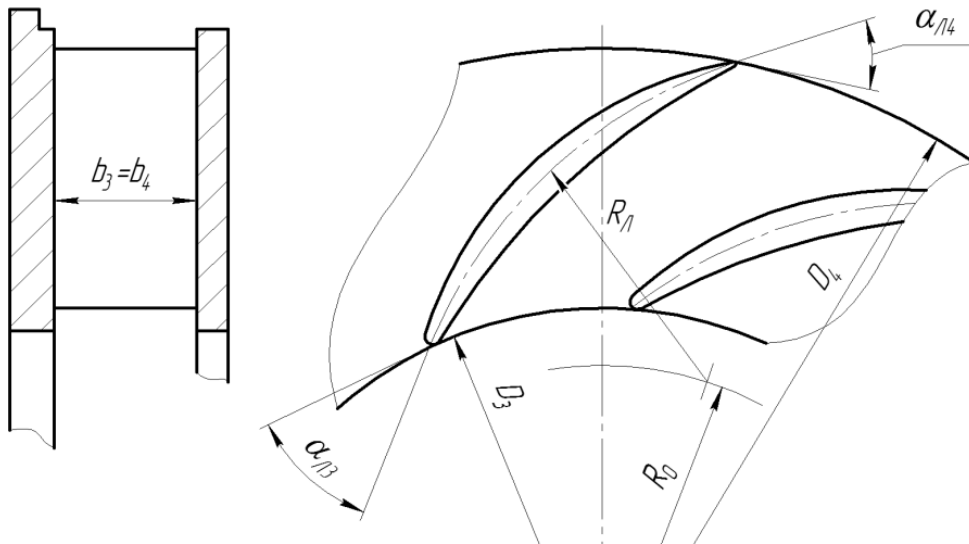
Схема колової гратки лопаткового дифузора
